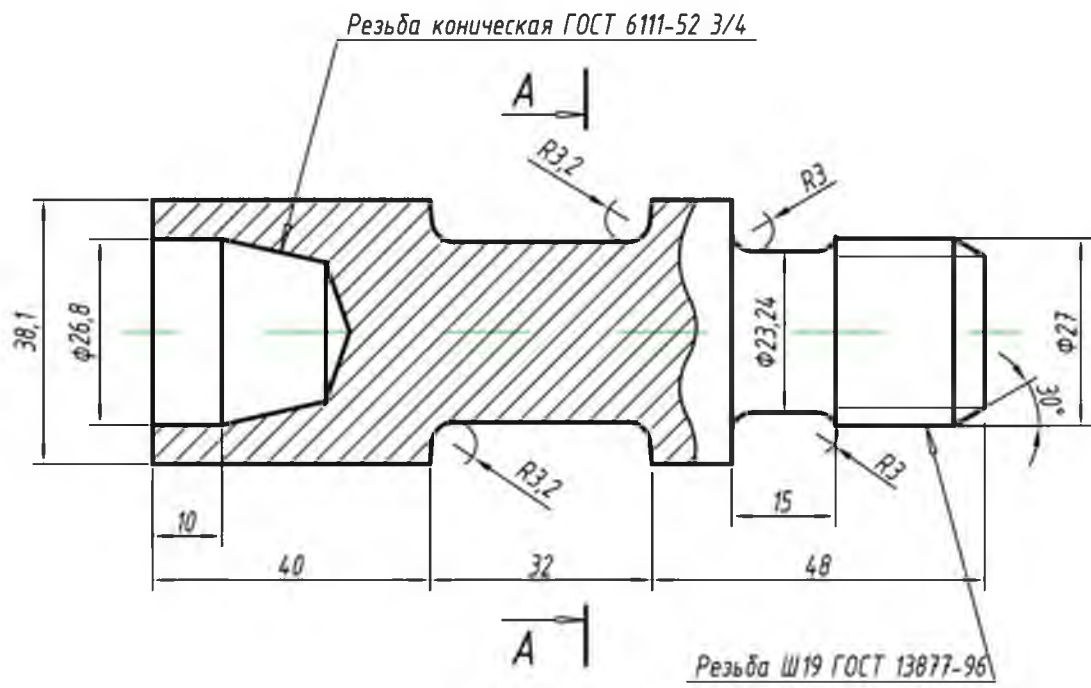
а - Тело штанги с цилиндрическим профилем резьбы
